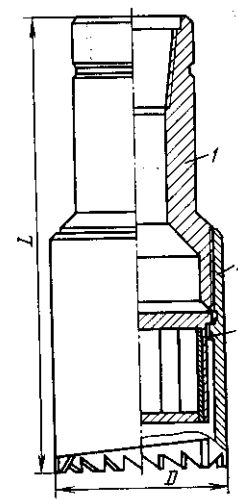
Магнитный фрезер-ловитель типа ФМ:
